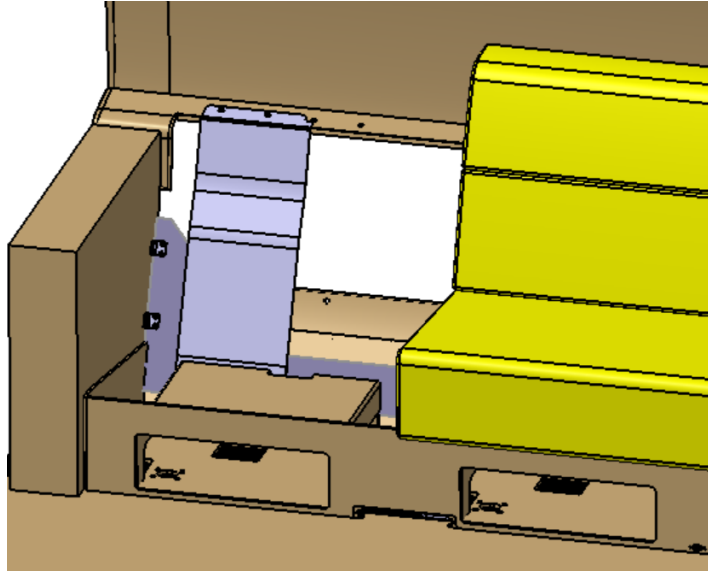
Montagem da Chapa Metálica (Fonte: o autor).
